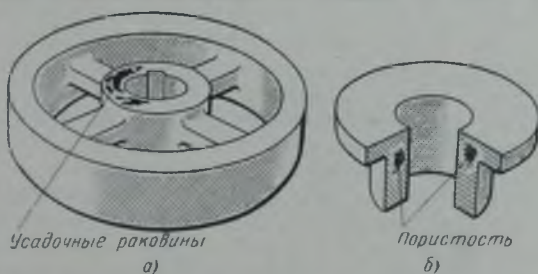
Отливки с усадочными раковинами и рыхлотой
